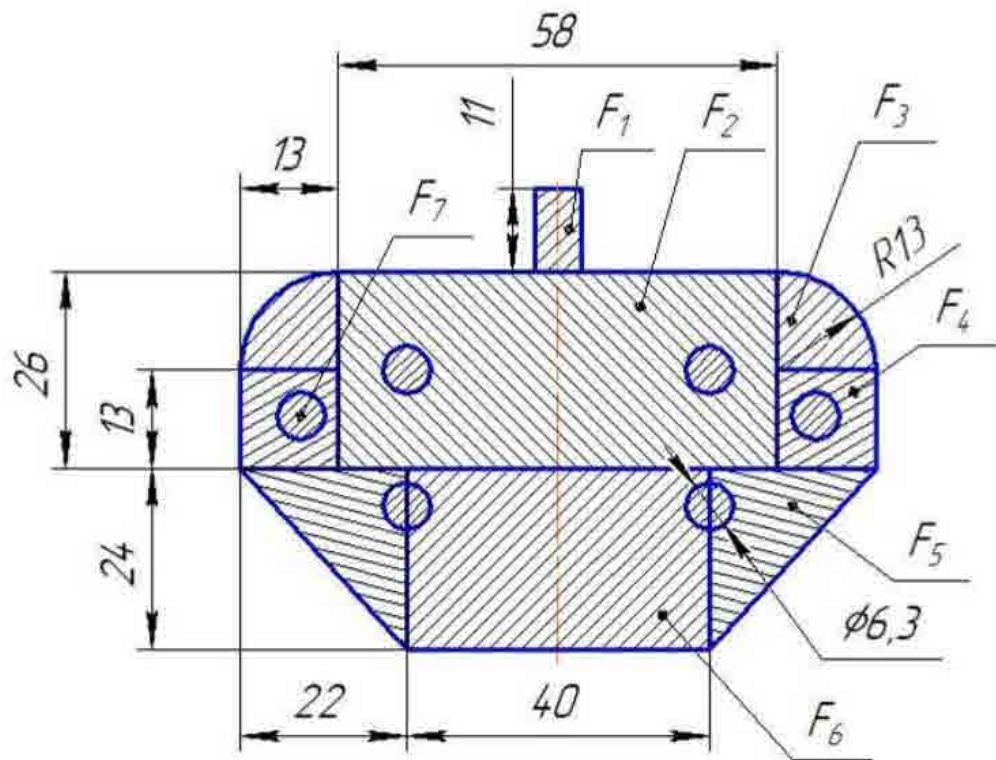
До розрахунку площі поверхні заготовки.
